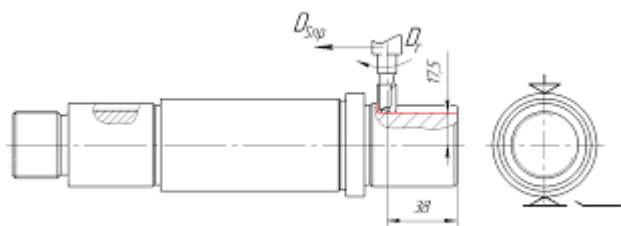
Изображение шпоночной фрезы на эскизе обработки
